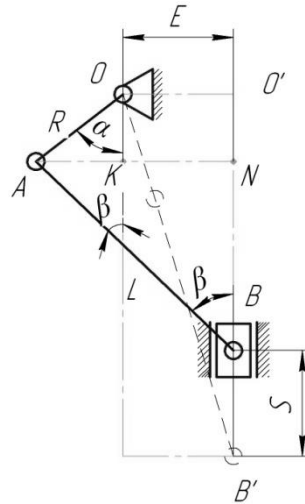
Схема дезаксіального кривошипно-повзунного механізму з верхнім приводом
